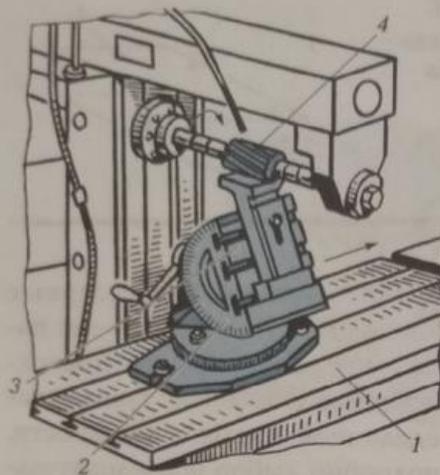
Фрезерование наклонной поверхности на универсальной поворотной плите:
